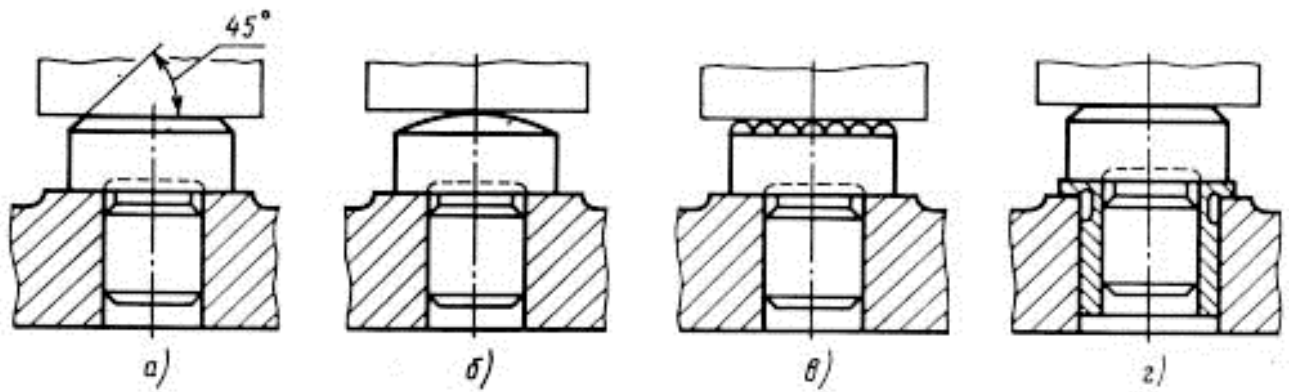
10. Опорные штыри (ГОСТ 13440-68, ГОСТ 13441-68, ГОСТ 13442-68): а – с плоской головкой для установки детали по обработанной поверхности;
